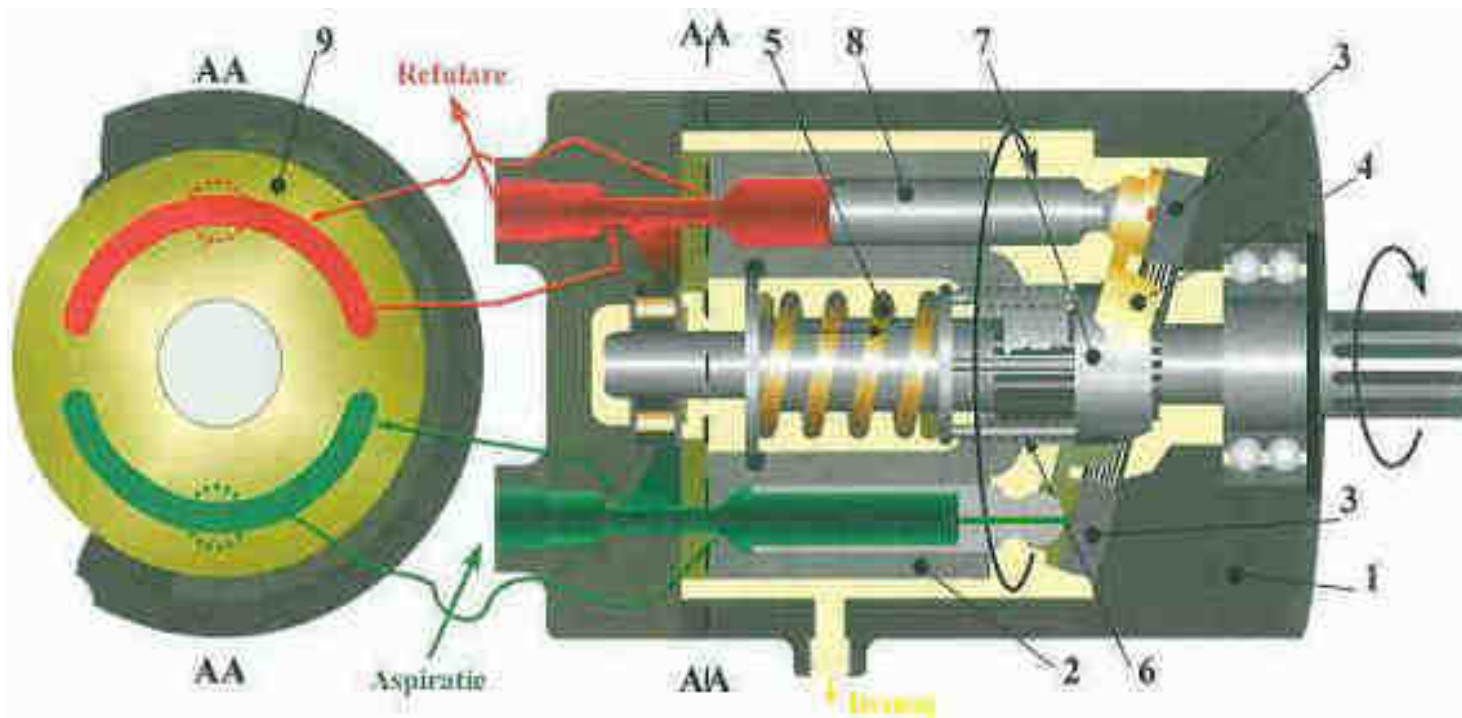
Pompe cu pistoane axiale și bloc înclinat
